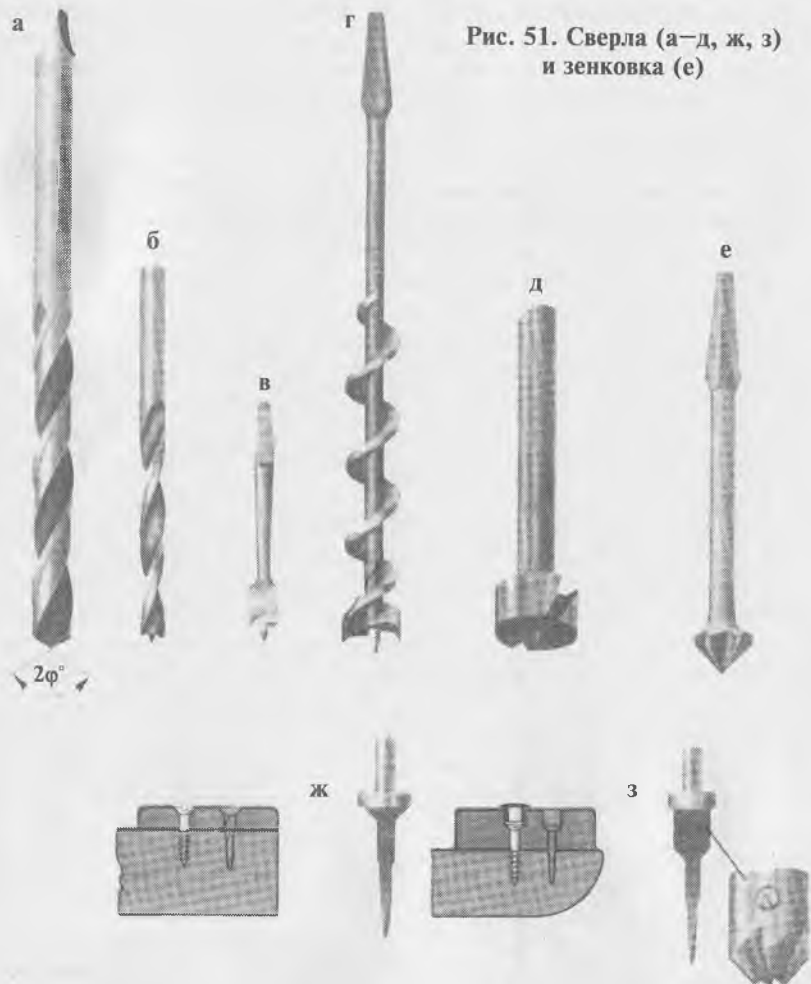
Сверла (а—д, ж, з) и зенковка (е)
